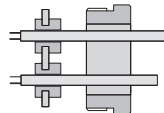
zu Schritt 1: Rändelschraube und Abdeckkappe
